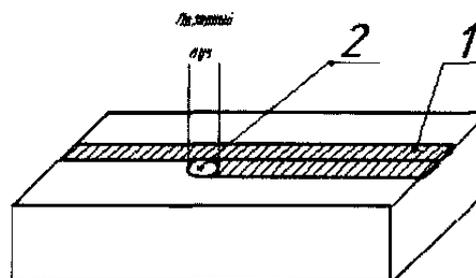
Лазерная закалка металла: 1 - зона закалки; 2 - пятно фокусировки лазерного излучения
